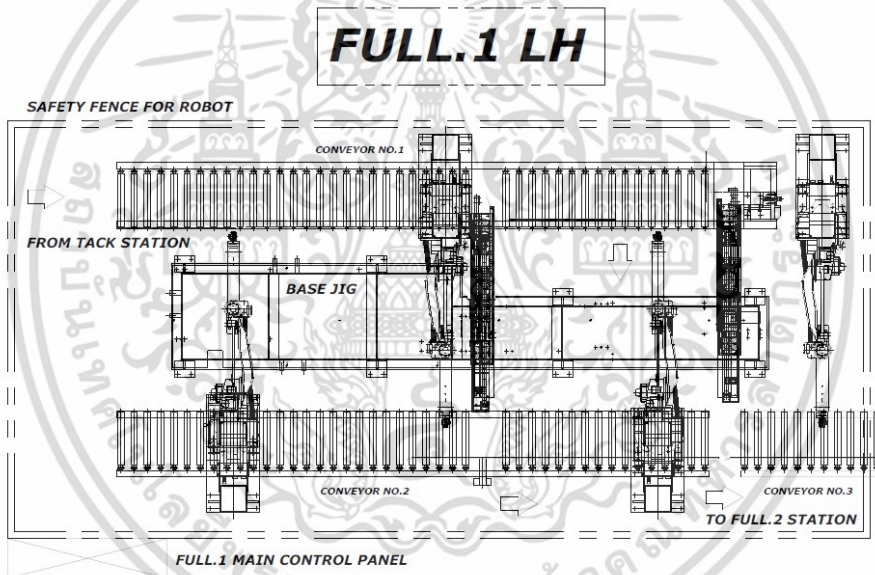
แบบ Jig Assembly Drawing (Top View)
